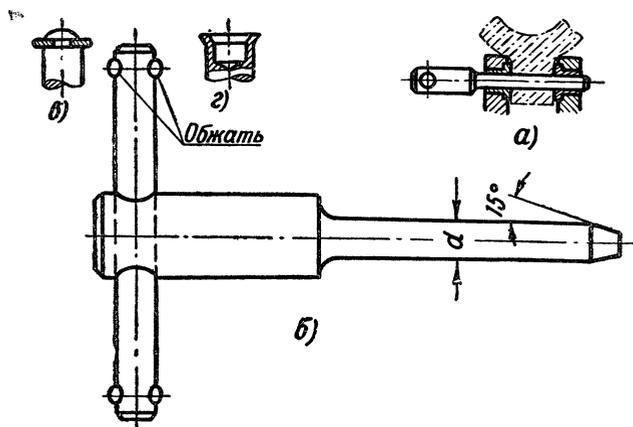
Фиксатор для установки трубок сварных хомутиков.
